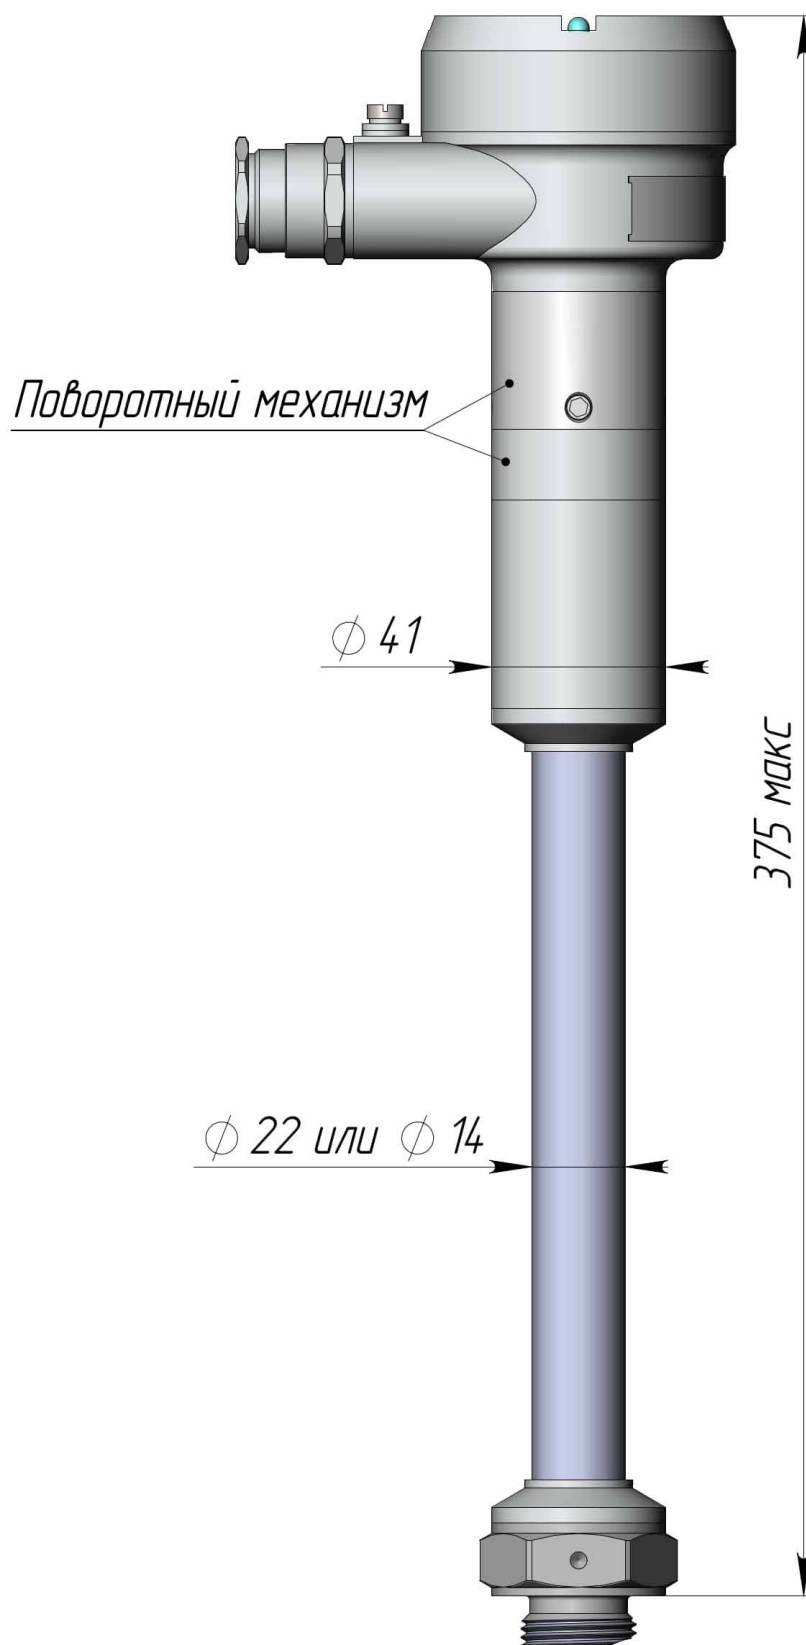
Габаритные размеры перехода на 450°C с поворотным механизмом
